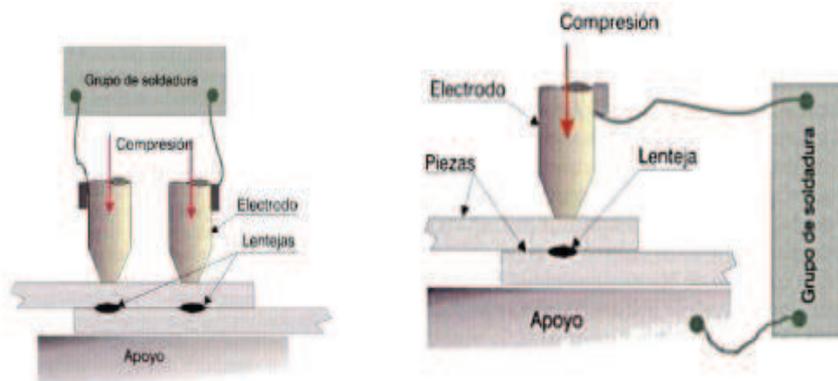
SOLDADURA POR PUNTOS
